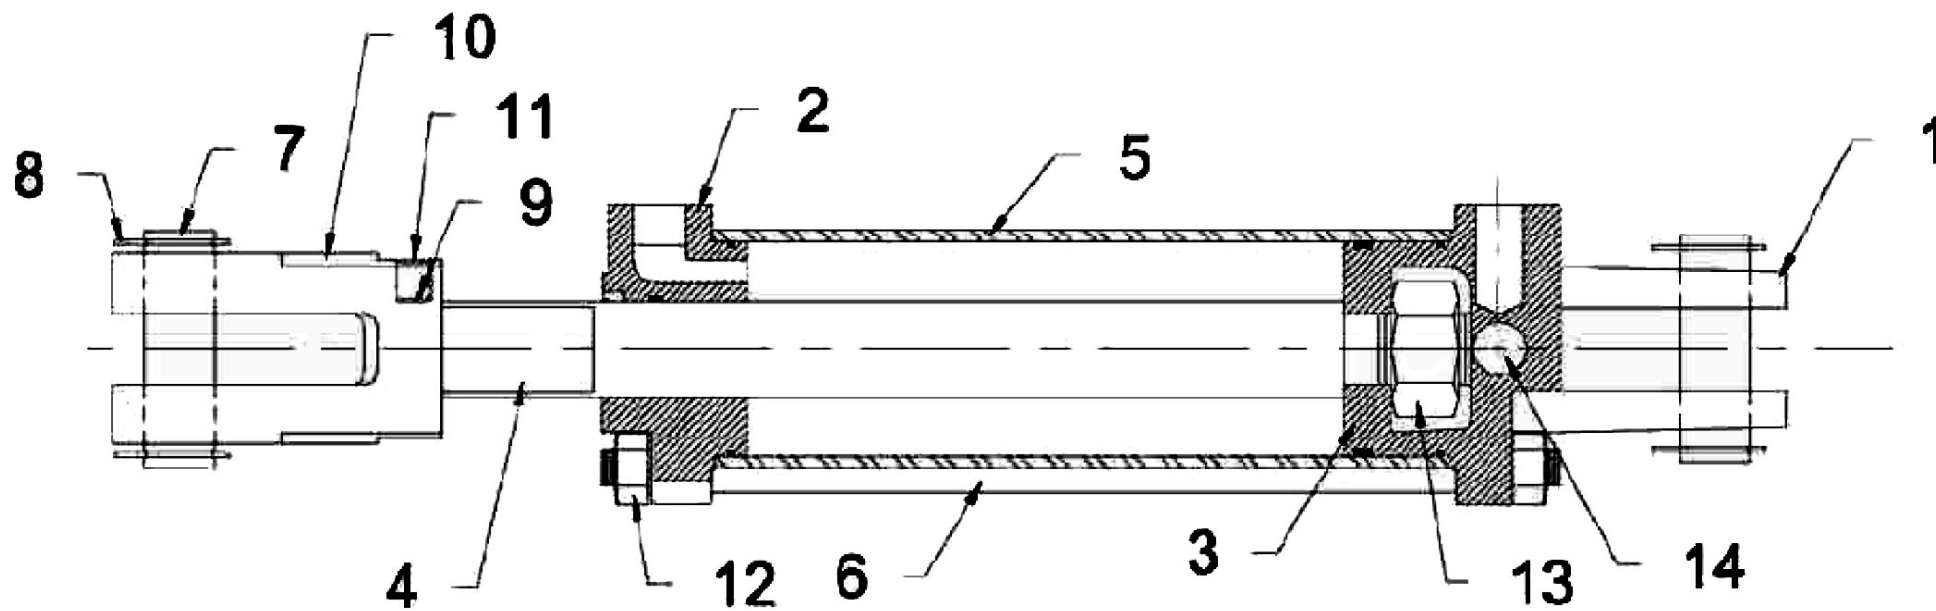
Чертеж гидроцилиндра Monarch (сцепка, направляющая и наклон)
